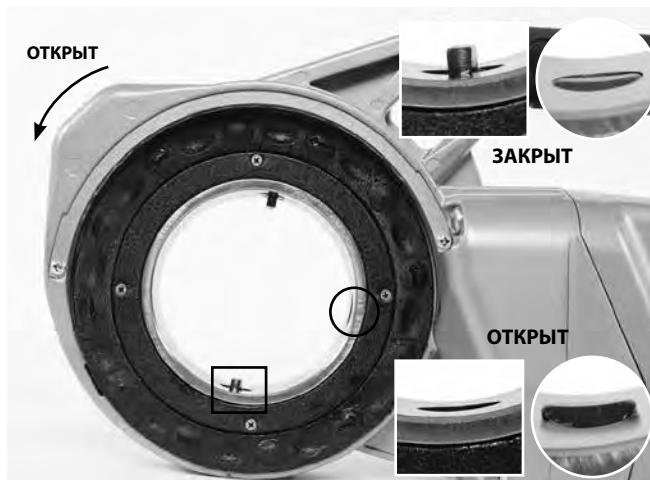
A - Стопорный механизм (760 FXP 12-R)
